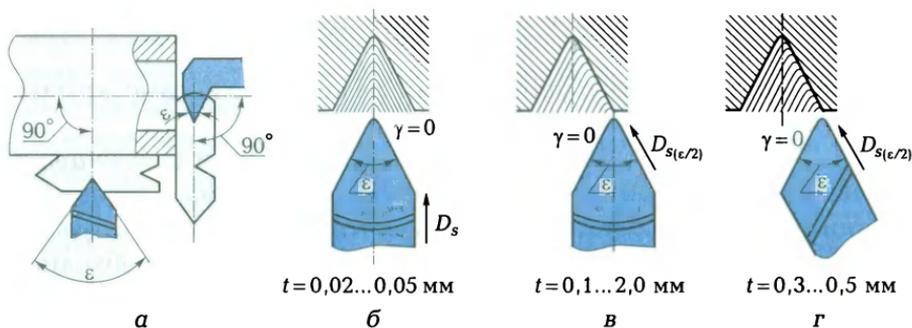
Схема установки резьбового резца по шаблону (а) и способы врезания резца при нарезании наружной резьбы в радиальном (б) и параллельном боковому профилю резьбы (в, г) направлениях:
